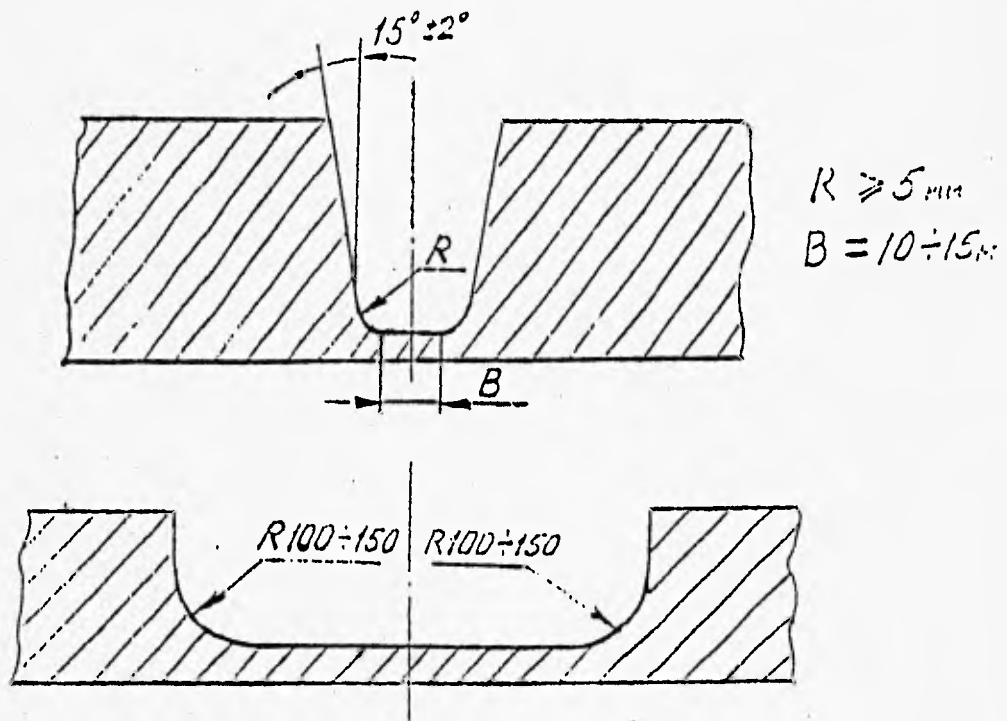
CARACTERÍSTICAS DE LAS ABERTURAS DE PLACA PARA REPARACIÓN.
